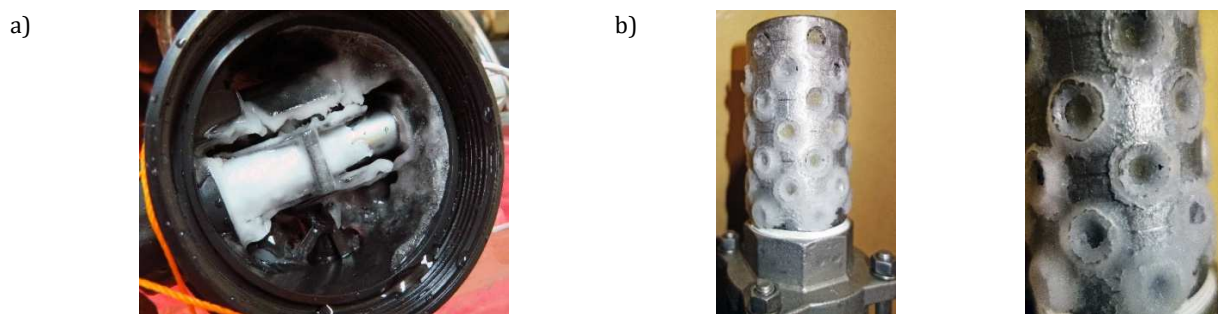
Przykłady elementów wykorzystywanych w układach techniki nurkowej o wadliwej konstrukcji:
